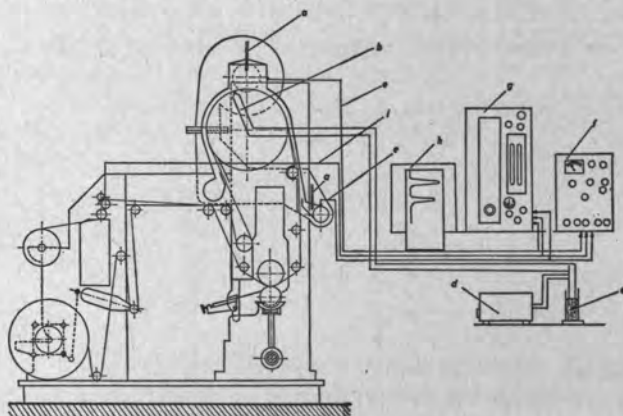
Seitenansicht der Versuchsmaschine mit stilisiertem Meßaufbau
